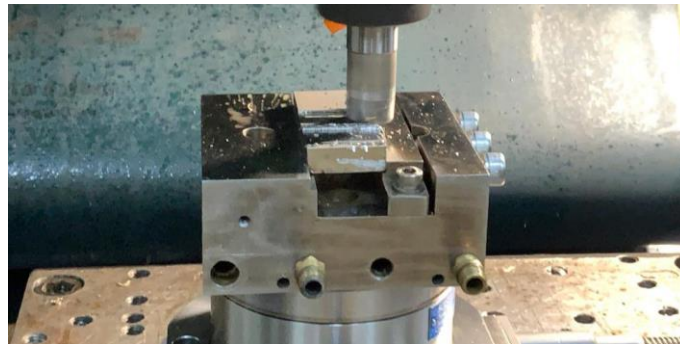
Montagem do dispositivo no centro de usinagem e fresamento do corpo de prova.
